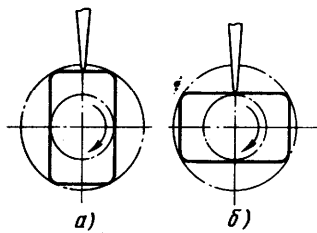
Схема электронно-лучевой сварки прямоугольного корпуса
